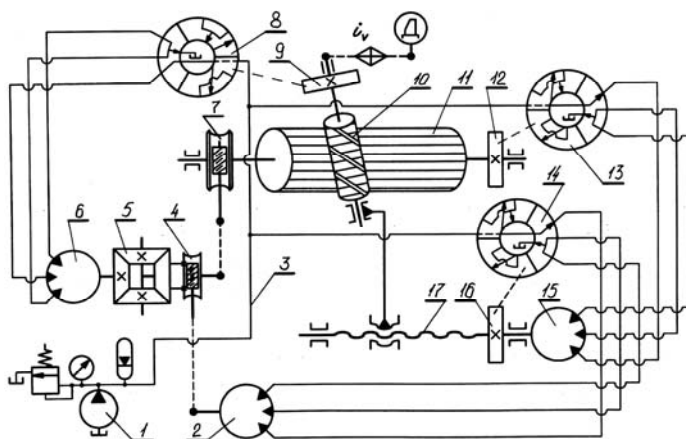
Структурная схема шлиффрезерного станка с гидравлическими связями в цепях деления продольной подачи
